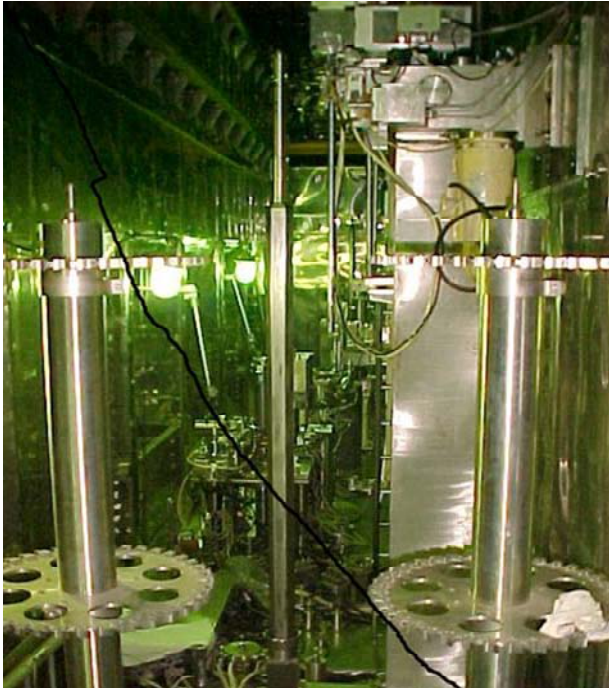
Внешний вид автоматизированной машины для изготовления ТВС
